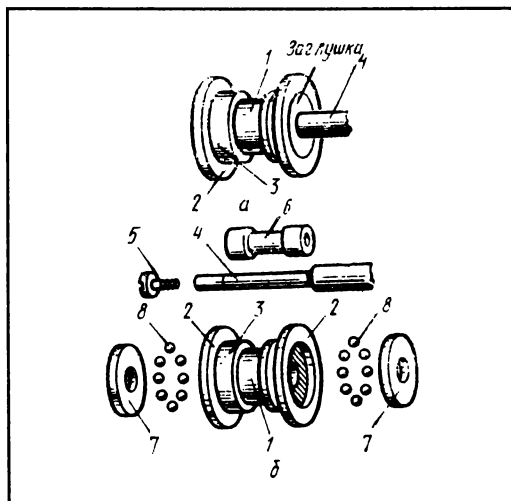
Направляющий ролик: а—в сборе; б—разобранный; 1—ролик, 2—бортик, 3—рабочий поясик, 4—ось, 5—торцовый винт, 6—распорная втулка, 7—заглушка, 8—шарики
